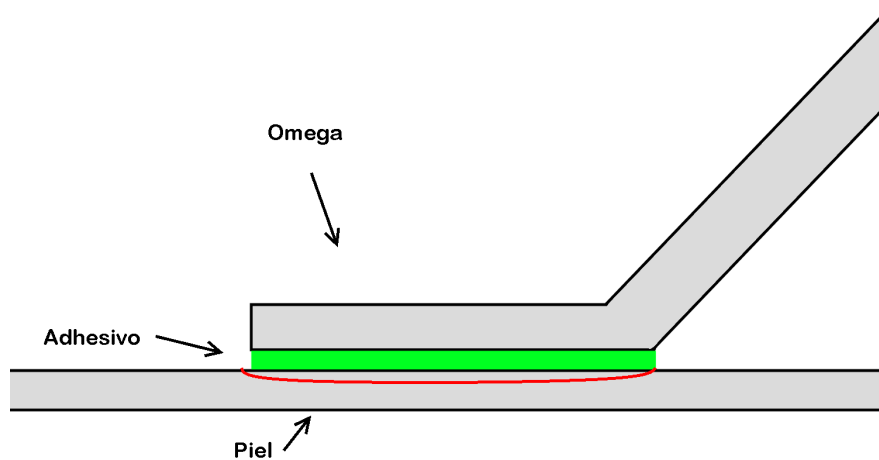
Detalle de la grieta de fallo en C-C2
